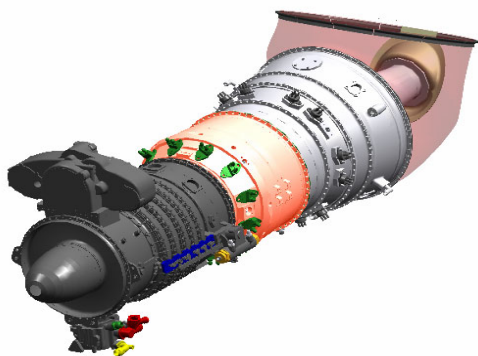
Промышленный газотурбинный двигатель ТВ3-137 (компоновка создана в Solid Edge)
